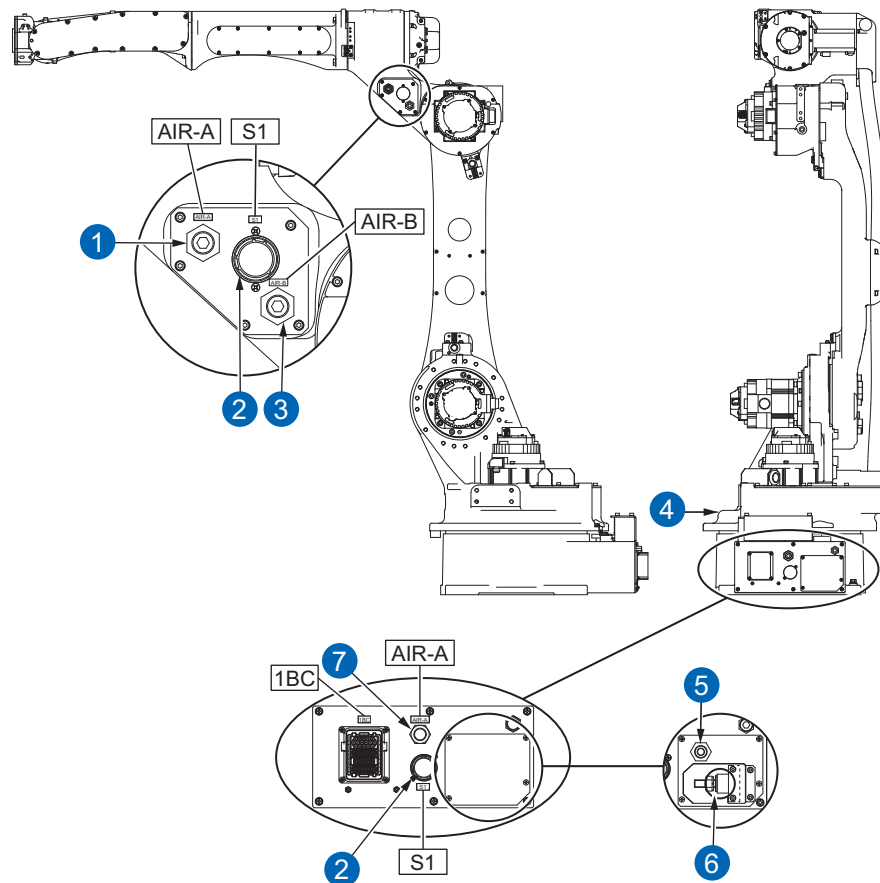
Anschlüsse für internen E/A-Kabelbaum und Druckluftführung
